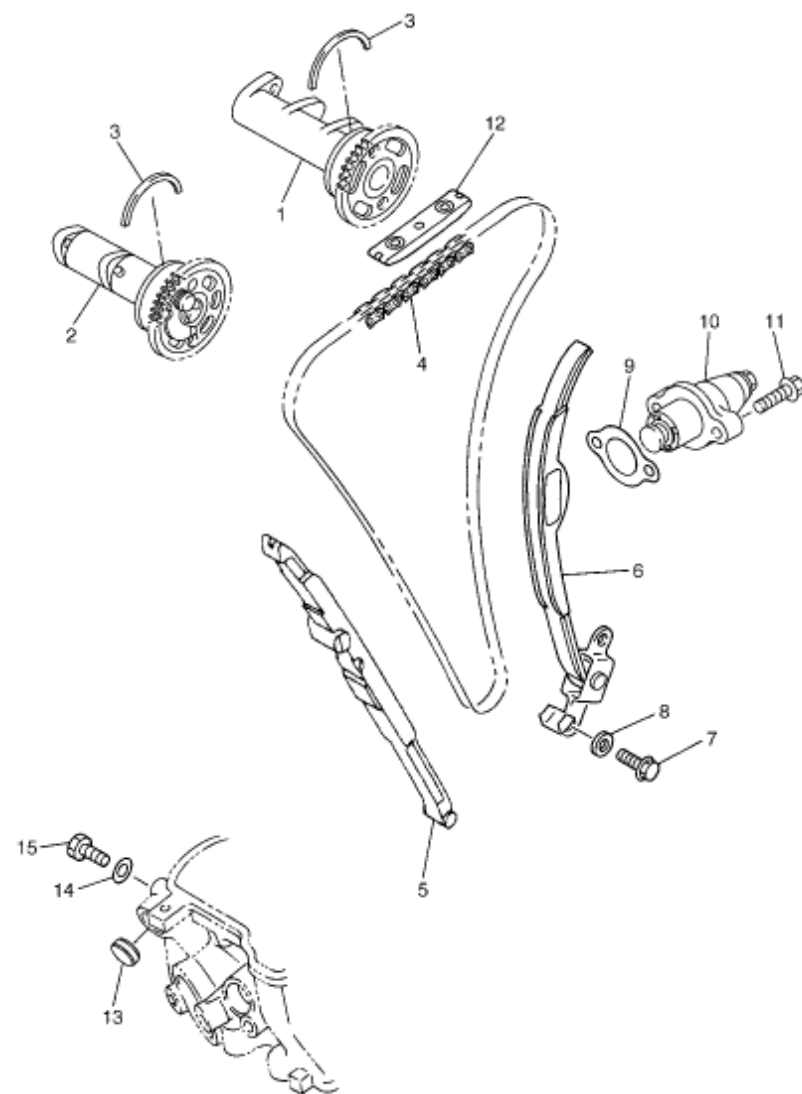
SOUPAPES / VALVE / VÁLVULAS
